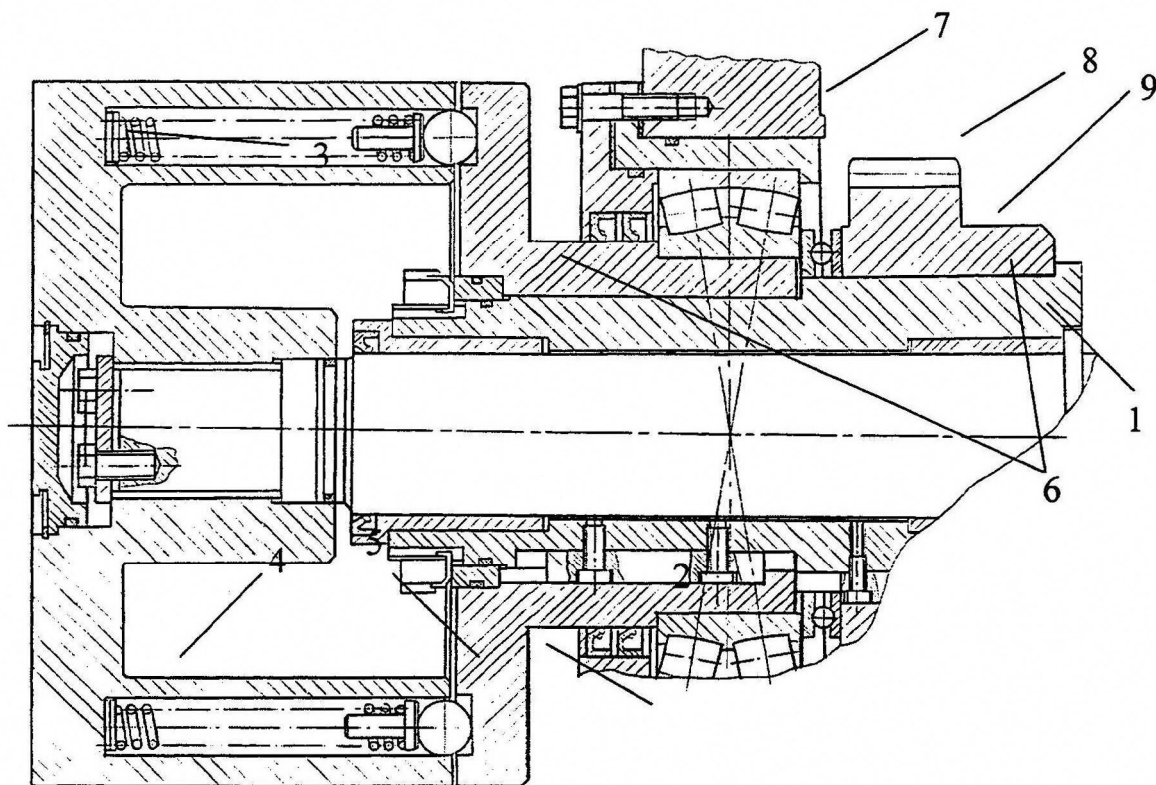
Конструкция шариковой предохранительной муфты на валу редуктора
